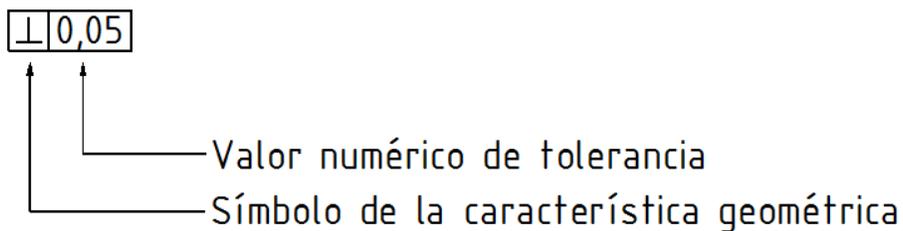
Cuadro de tolerancia geométrica con dos casillas.
